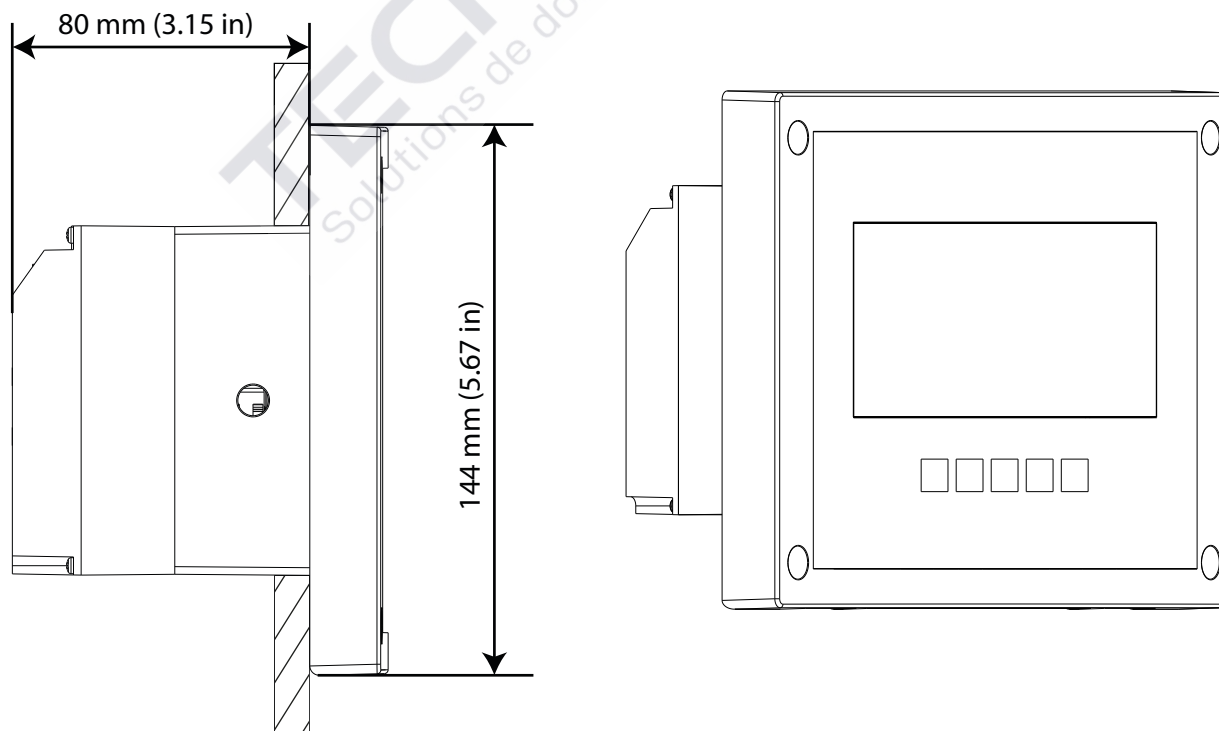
Découpe et dimensions du panneau pour le dispositif à montage sur panneau Snail Lock System
